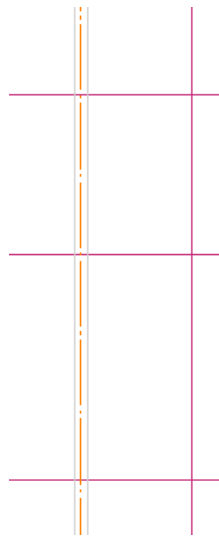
Попереднє креслення з допоміжними горизонтальними прямими
